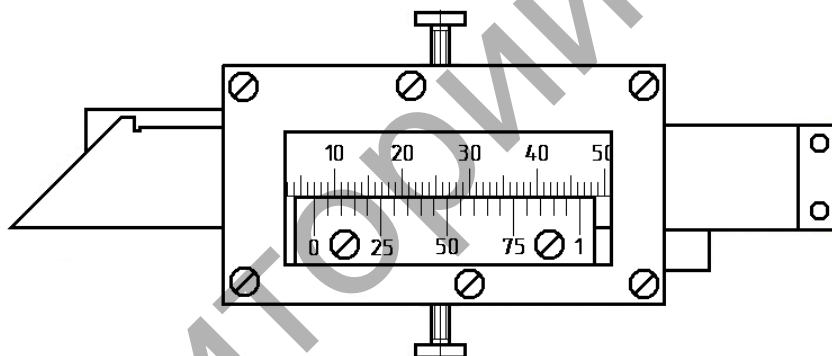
Универсальный фаскомер ИФУС на основе штангенциркуля
